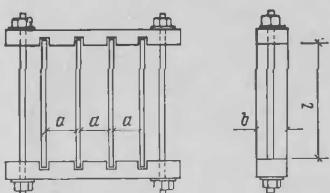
Схема металлической формы для цементных балочек (а, б — размеры поперечного сечения балочек; 1 — длина балочек)
